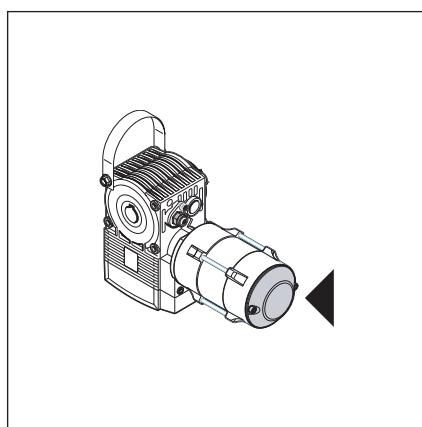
Wellenantrieb mit Abdeckkappe
